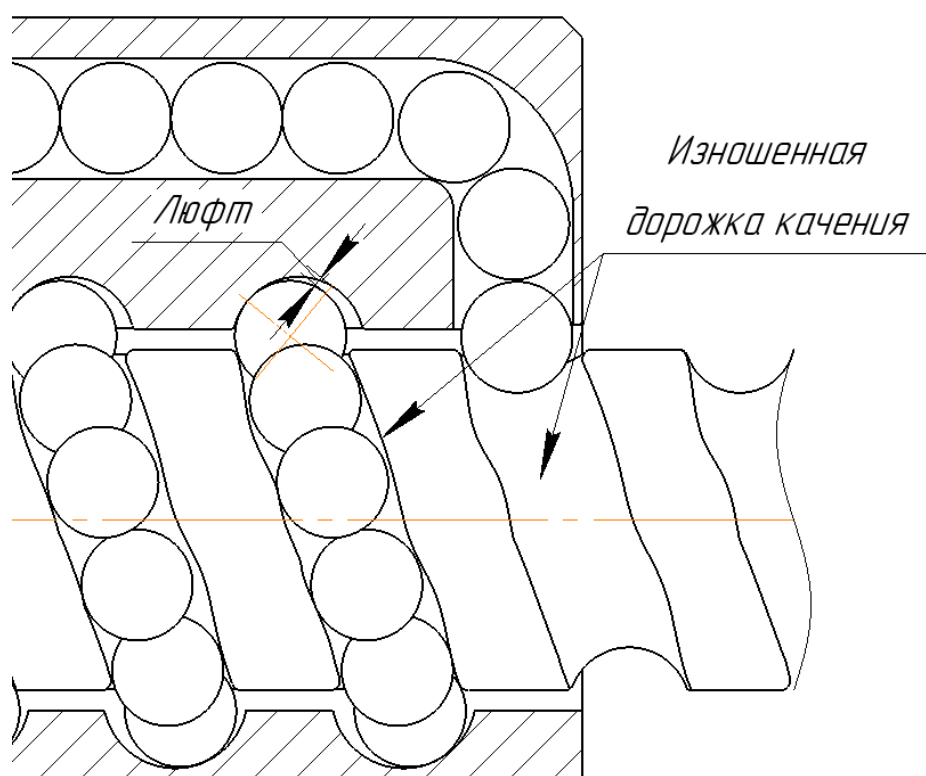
Люфт и износ шариковинтовой передачи
